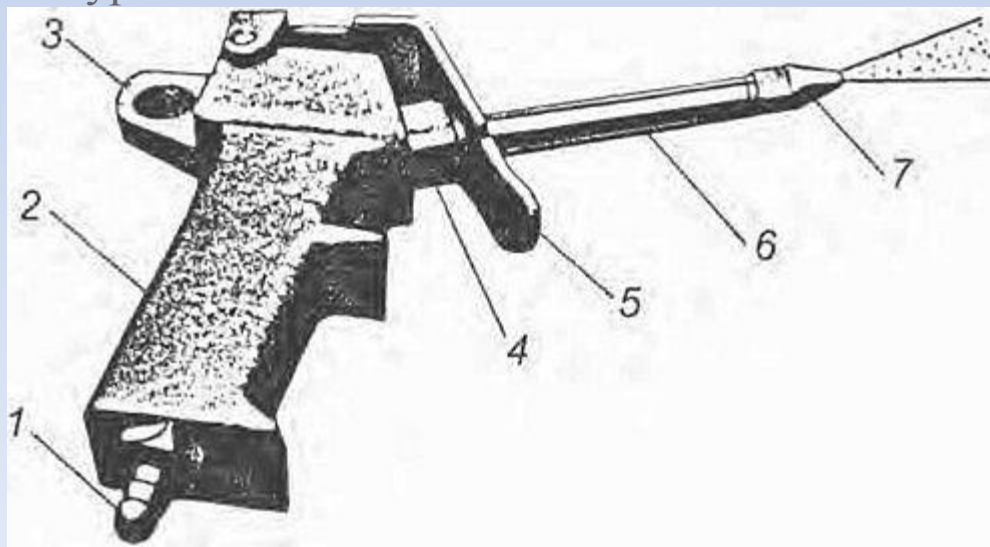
Пистолет для обдувки деталей сжатым воздухом мод. С-417
